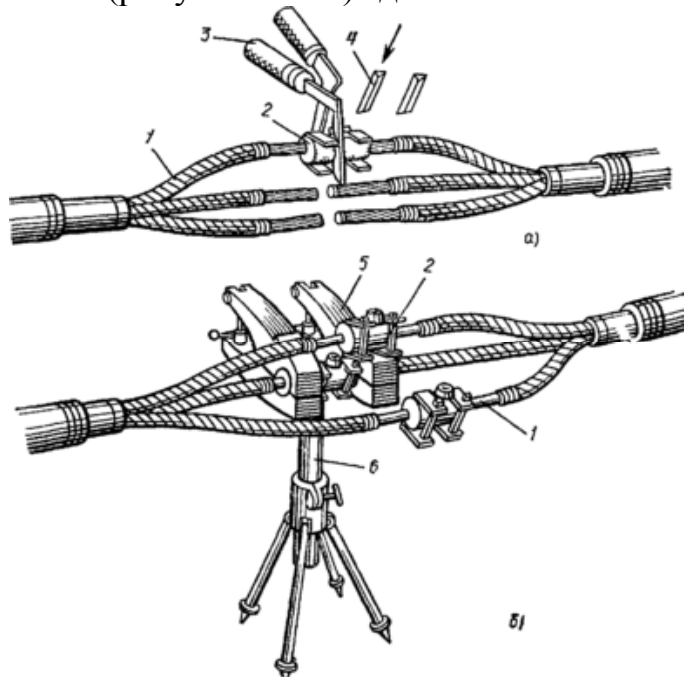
Пропано-кисневе зварювання в стик алюмінієвих жил перетином від 16 до 240 мм²: а - установка зварювальних форм; б - установка і закріплення охолоджувачів; 1-жила; 2 - зварювальна форма; 3 - струбцина, 4 - клини; 5 - охолоджувач, 6 - опорна стойка
